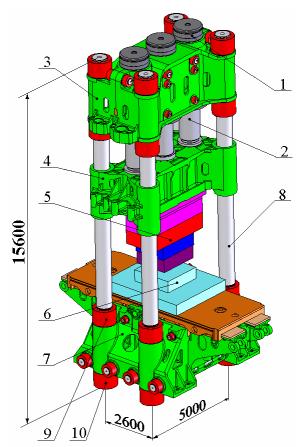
Гидравлический пресс конструкции УЗТМ силой 60 МН 1 — гидроцилиндр; 2 — плунжер; 3 — поперечина верхняя; 4 - подвижная поперечина; 5 - плиты верхнего штампового набора; 6 — плиты нижнего штампового набора; 7 — основание; 8 — колонна; 9 — гайка внутренняя; 10 — гайка внешняя
